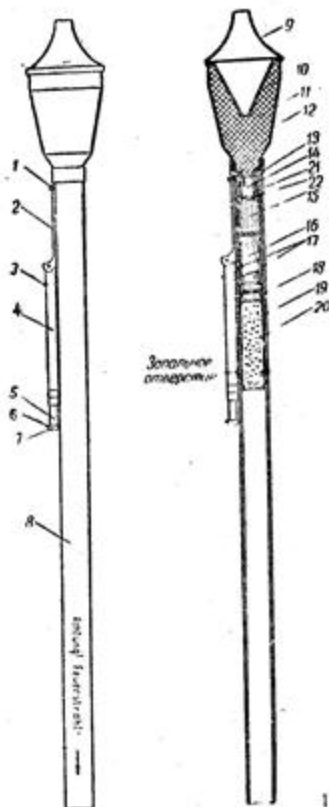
Реактивное противотанковое приспособление малого образца — «Фаустпатрон-1»:
